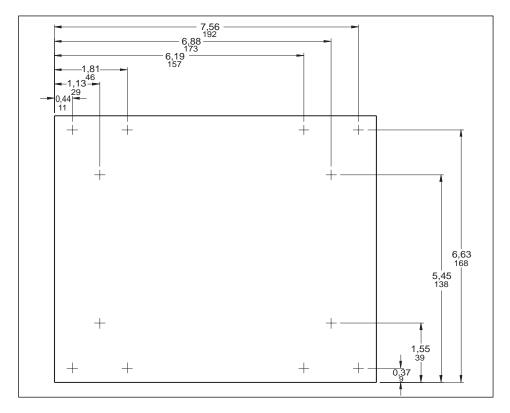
Montaje elevado: Agujeros de los soportes en L
